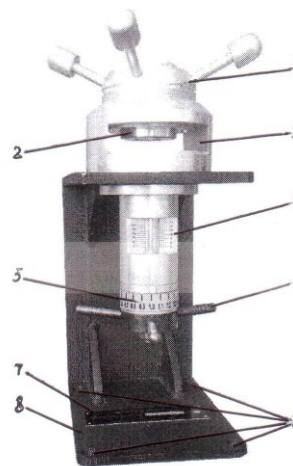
Штамп Еріксена NOVOTEST SHE-1: 1 – поворотний притискний пристрій; 2 – матриця; 3 – прорізь для зразків; 4 – пристрій розрахунку глибини вдавлювання пуансона (вертикальна шкала); 5 – пристрій розрахунку глибини вдавлювання пуансона (кругова шкала); 6 – кермо; 7 – маркування; 8 – станина; 9 – отвори для фіксування приладу
